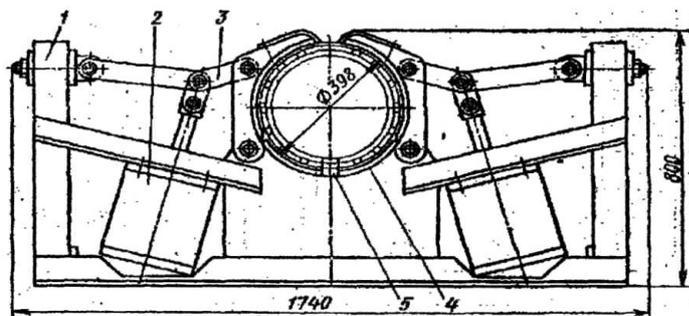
Приспособление для сборки продольных стыков обечаек малого диаметра
